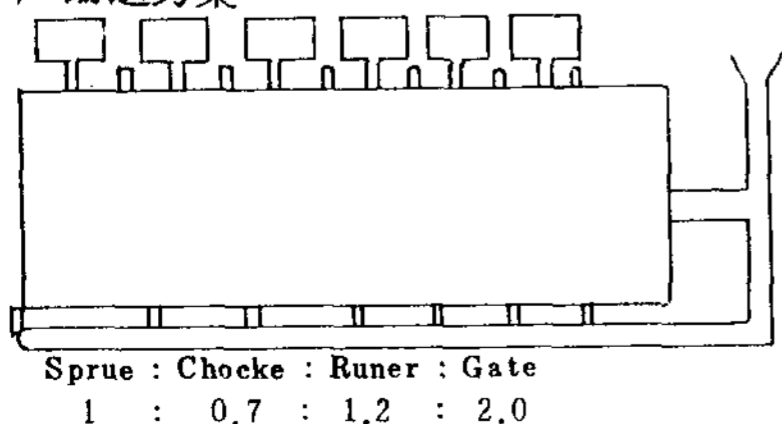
Diesel Engine 의 Cylinder Block 의 주조방안
